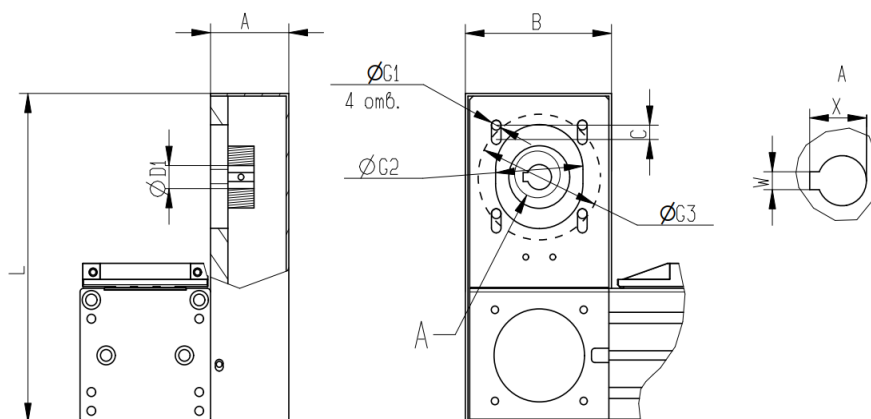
Набор для параллельной установки редуктора PR-MCR-80.
